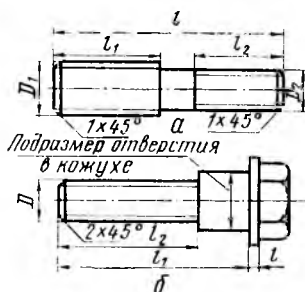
Ступенчатые шпилька (а) и болт (б).
